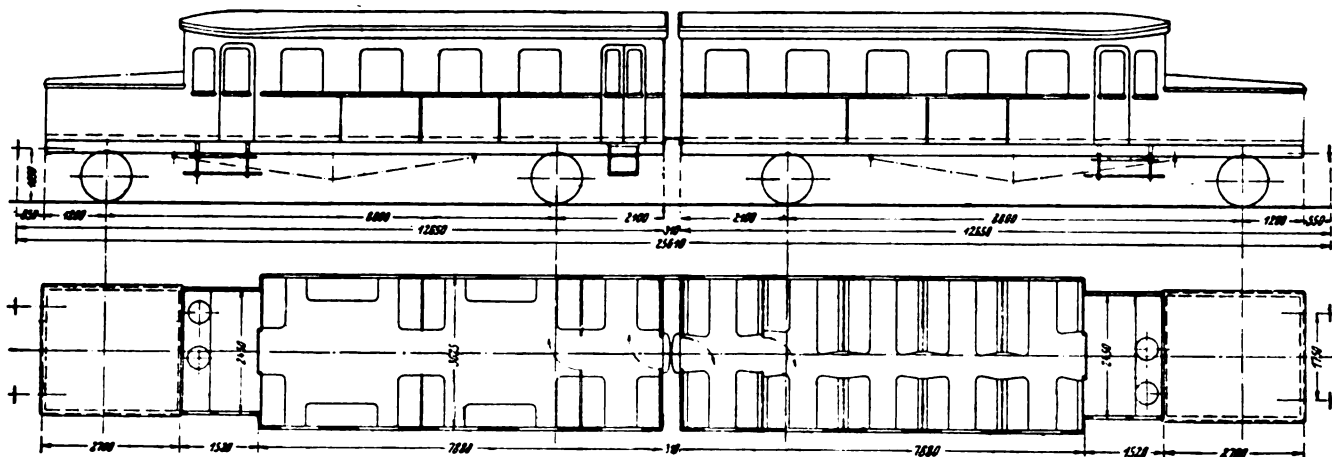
e 11. — Automotrici ad accumulatori, delle Ferrovie di Stato Prussiane - *Elevazione e pianta.
